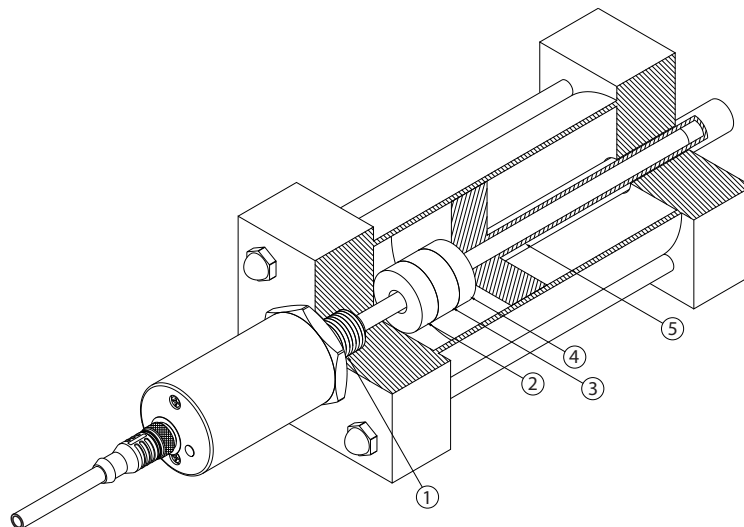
Gerät in einen Hydraulikzylinder montieren
